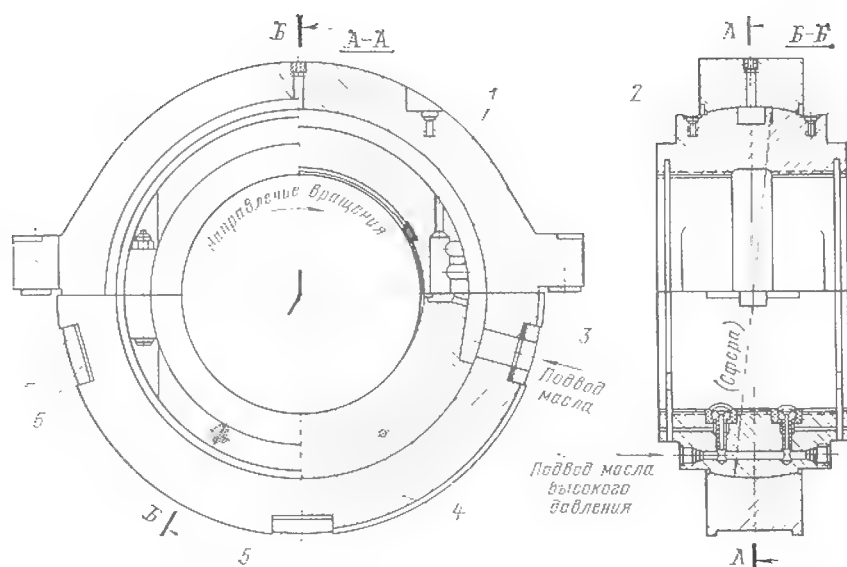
Опорный подшипник турбины К-500-65/3000 ХТЗ:
